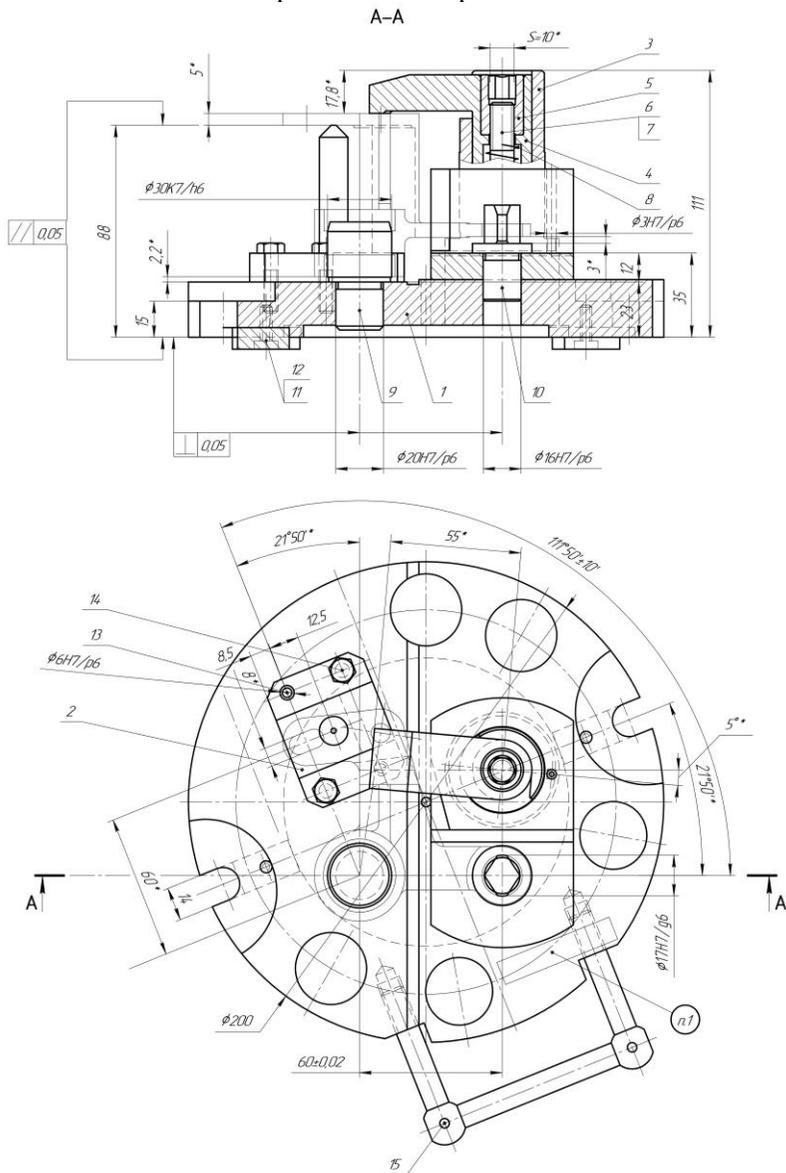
Сборочный чертёж приспособления для фрезерования паза
